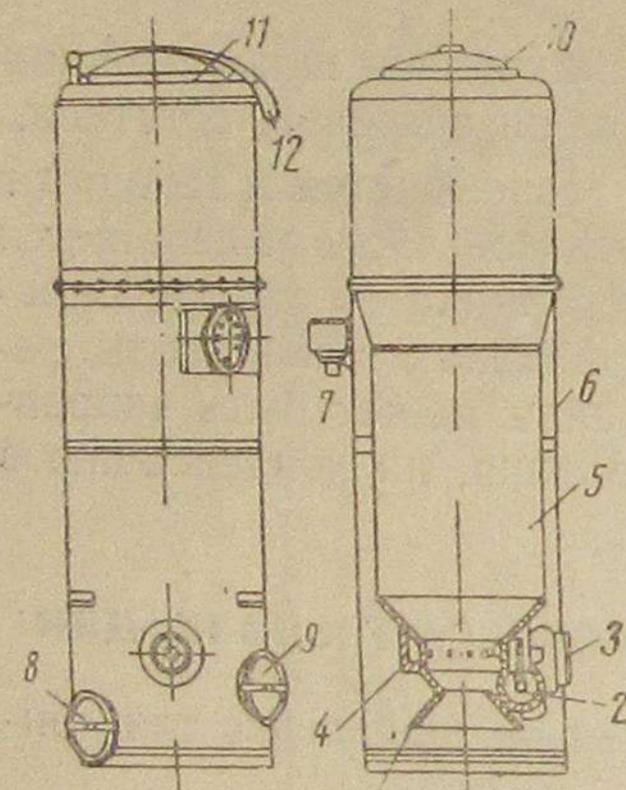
Газогенератор обращенного процесса для двигателя ГАЗ-42
